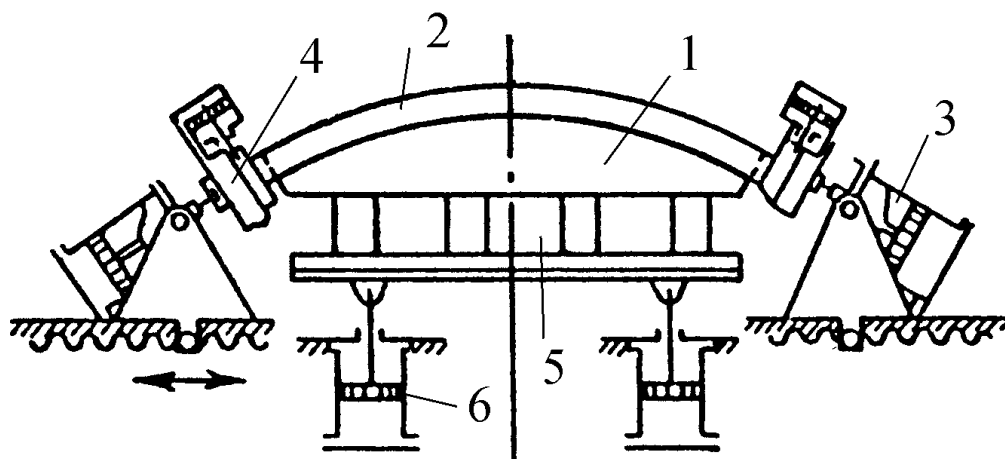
Схема розтяжно-обтяжного преса: 1 – обтяжний пуансон; 2 – заготованка; 3 – гідроциліндри; 4 – затискачі; 5 – стіл; 6 – силовий циліндр преса
